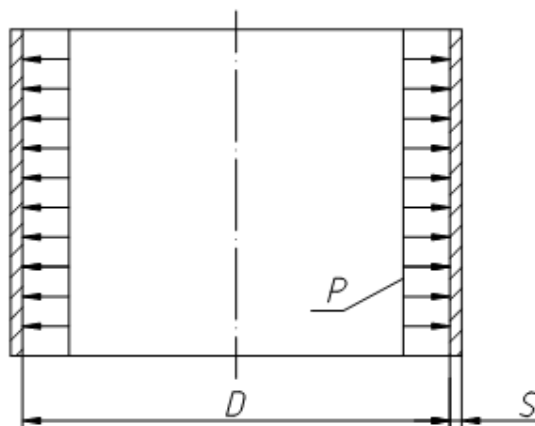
Розрахункова схема циліндричної обичайки апарату
